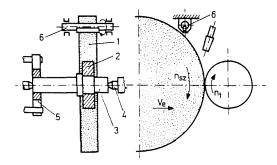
1. Шлифовальный круг; 2. Образец; 3. Оправа для зажима; 4. Динамометр; 5. Поводок; 6. Приспособление к взятию пробы для определения износа круга
